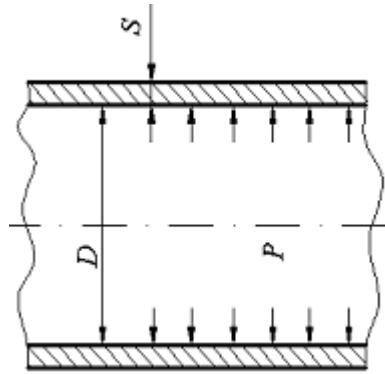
Розрахункова схема циліндричної обичайки
